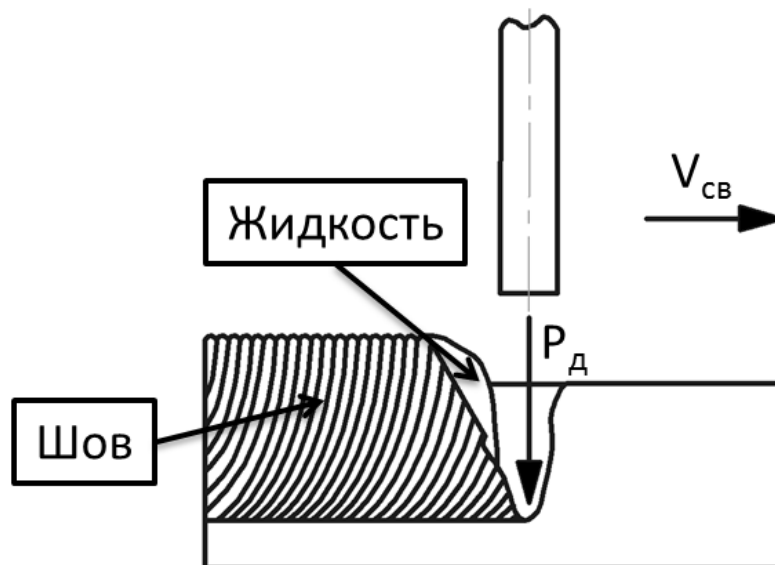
образование кратера на поверхности сварочной ванны
